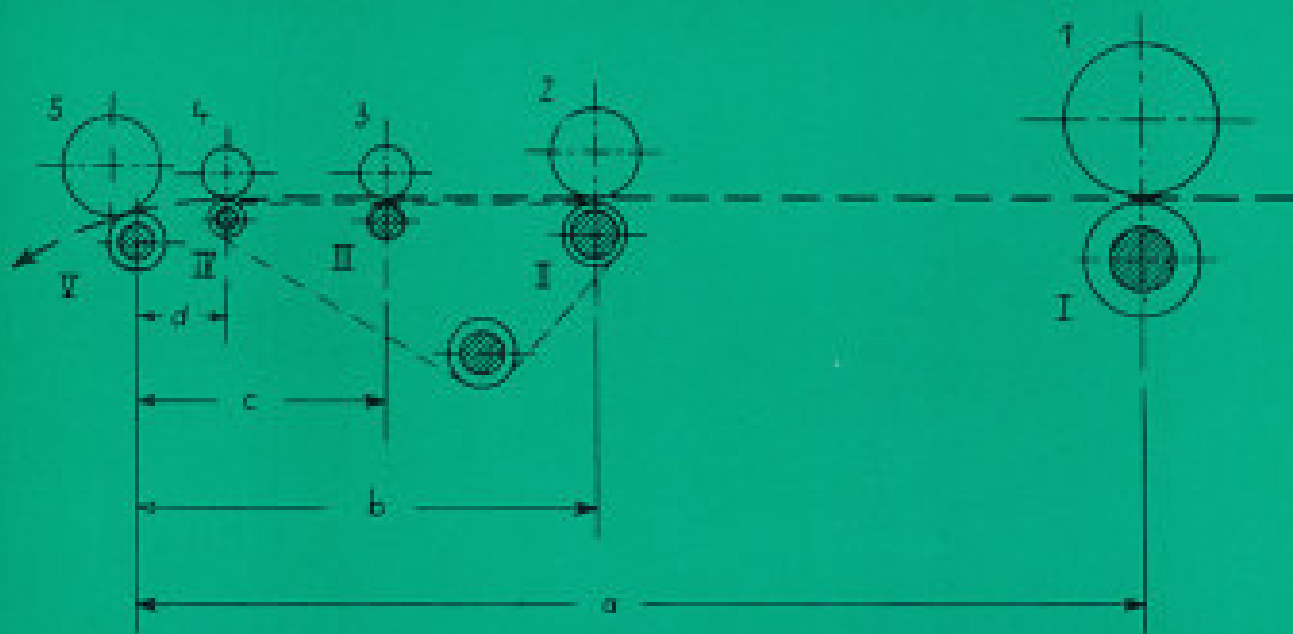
Stadienwerkzeuge der Ringspinnmaschine
